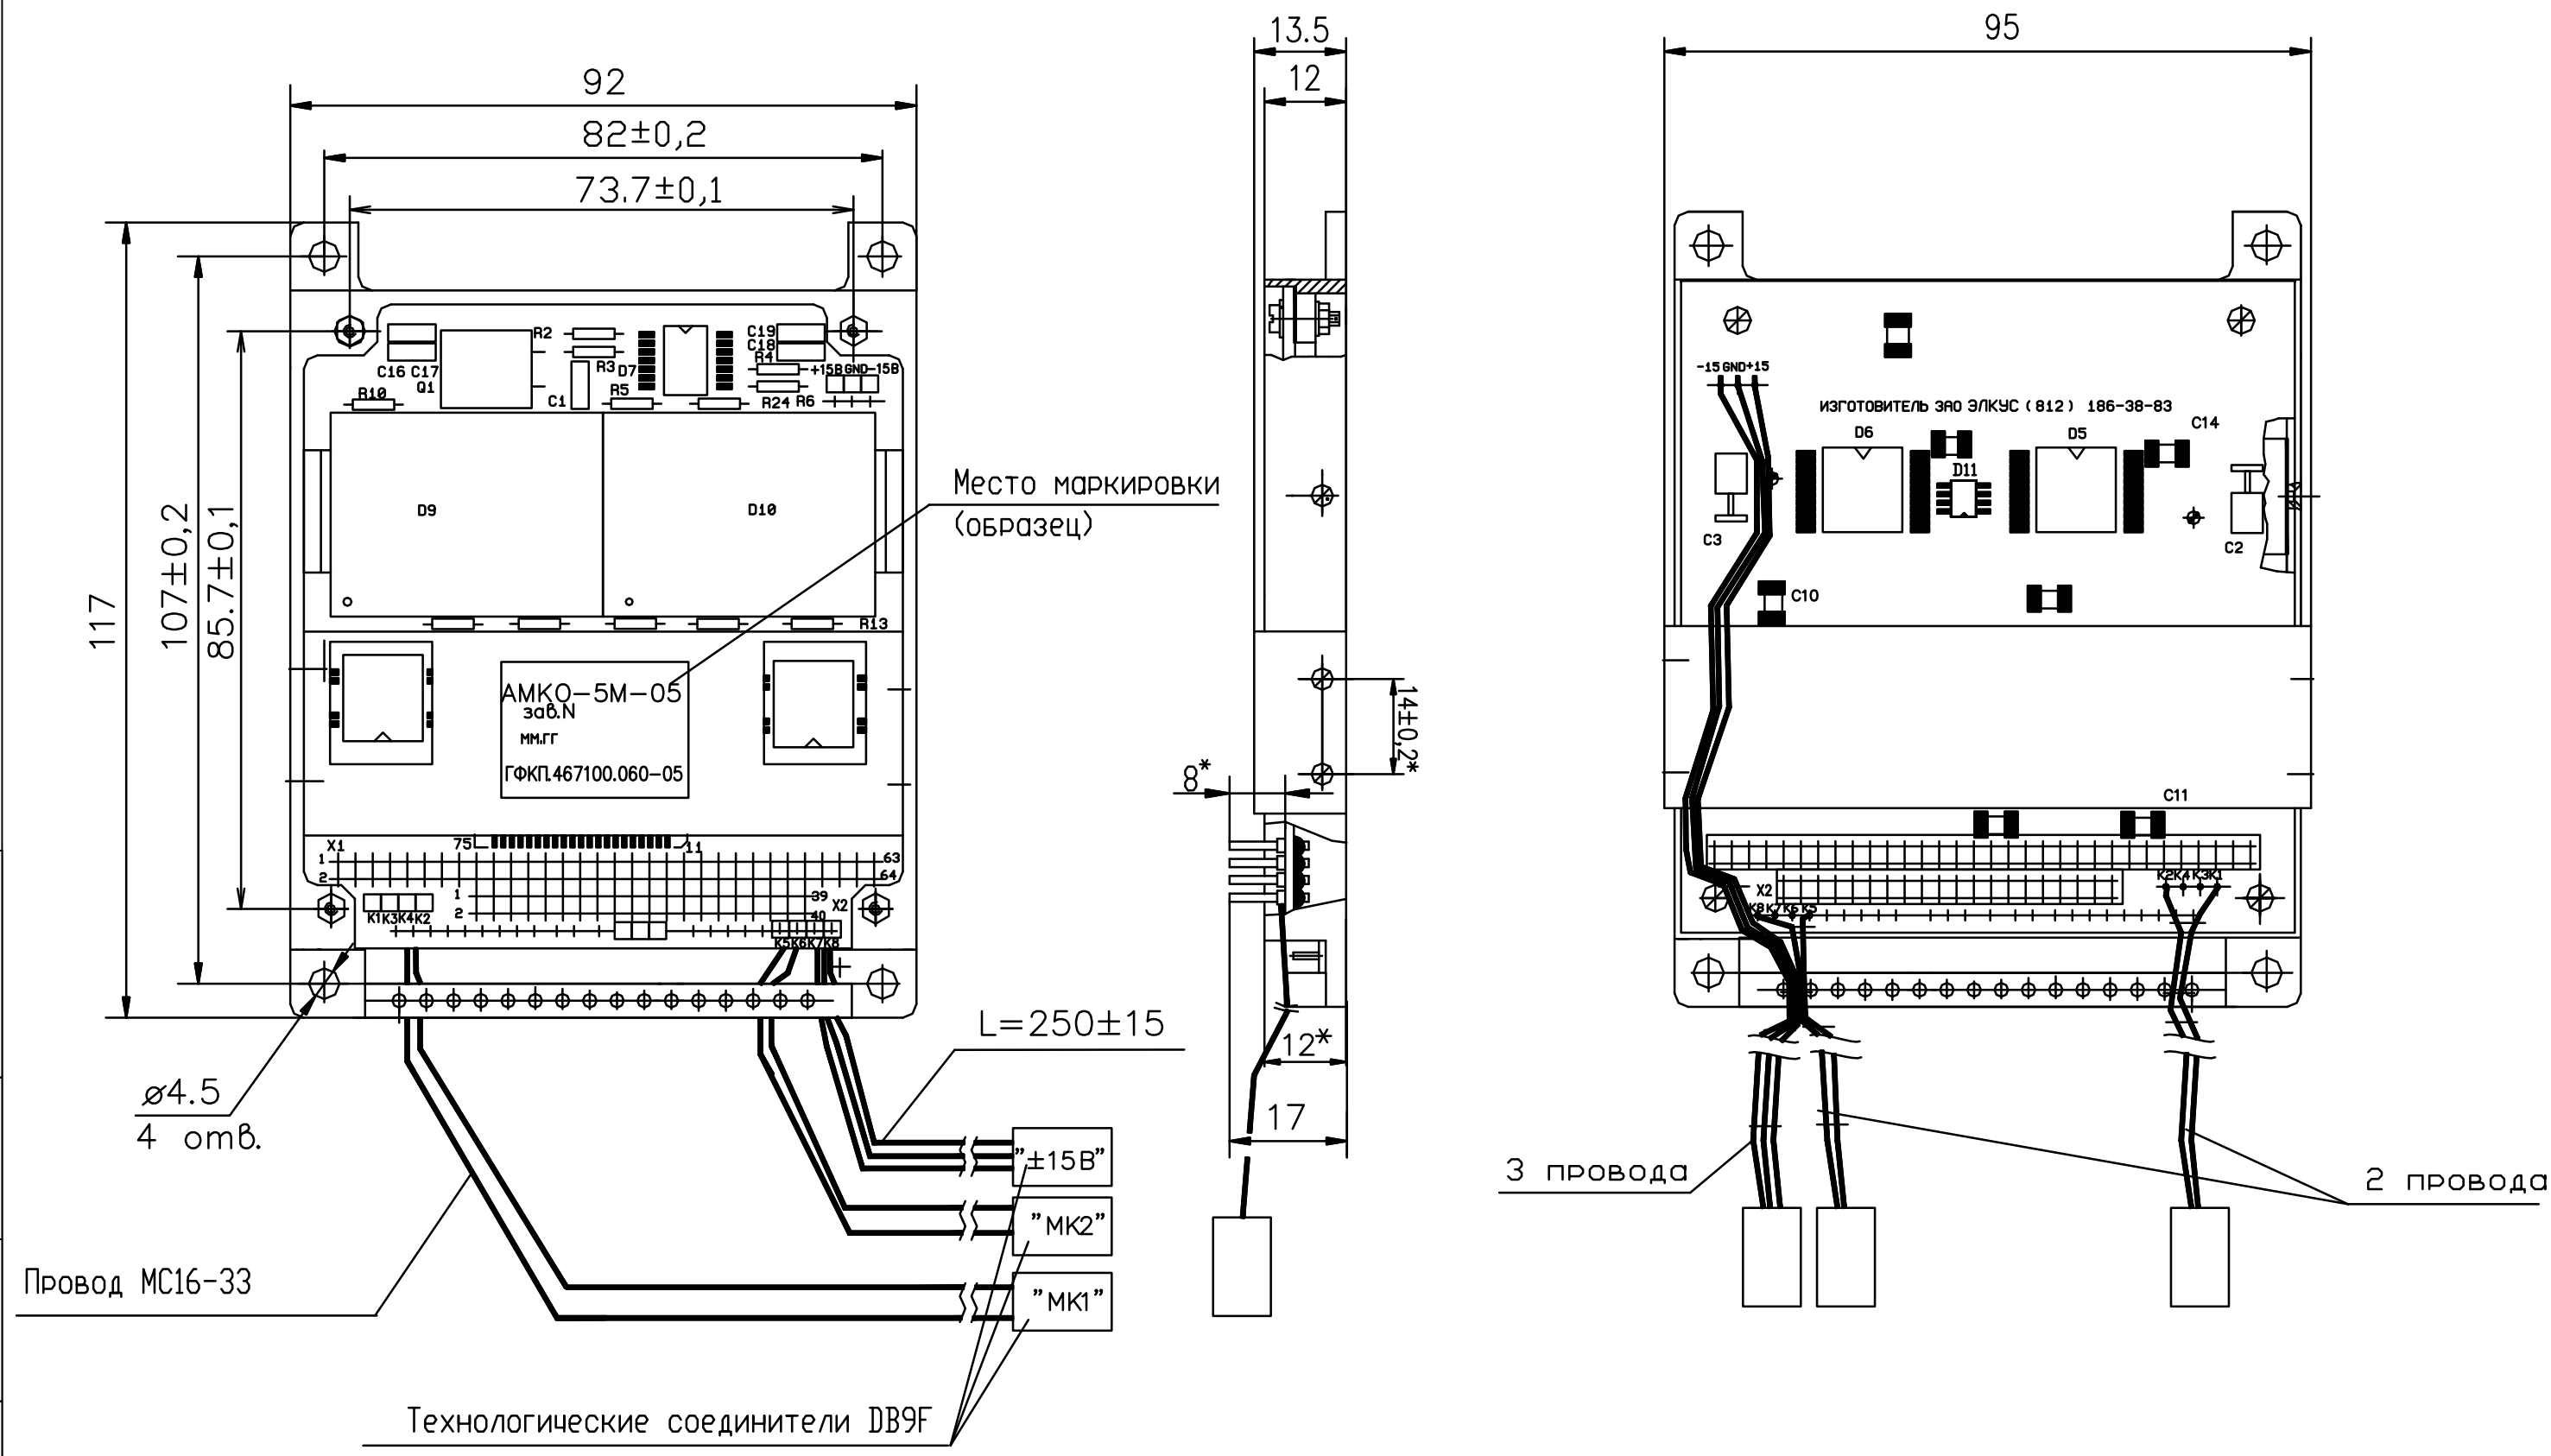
Габаритный чертеж исполнения АМКО-5М-05
